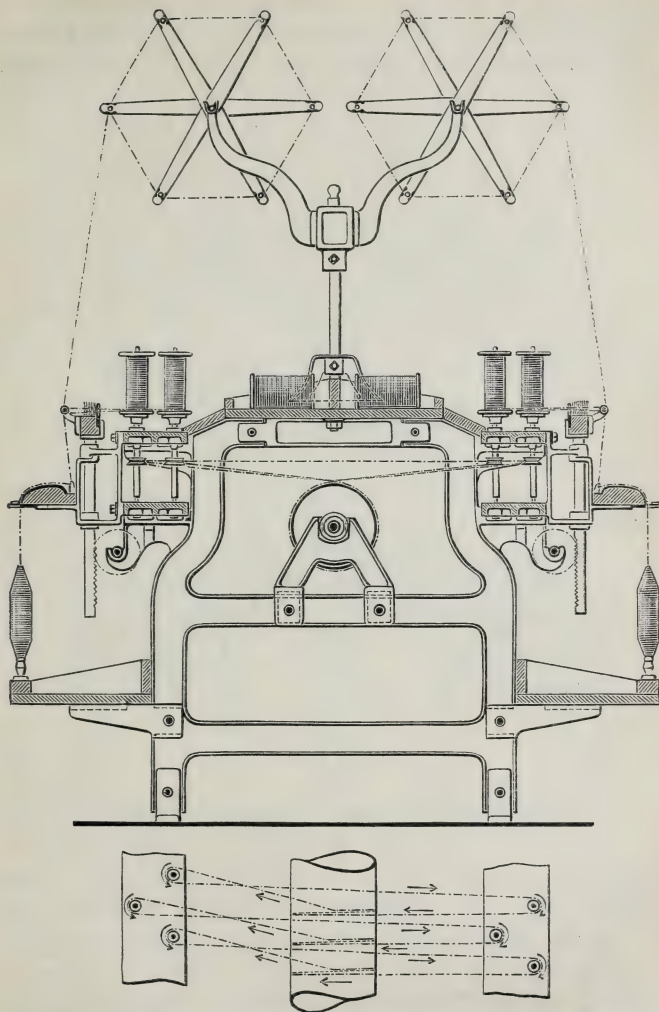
Kettenspinnmaschine mit stehenden Spindeln: Seitenansicht.
